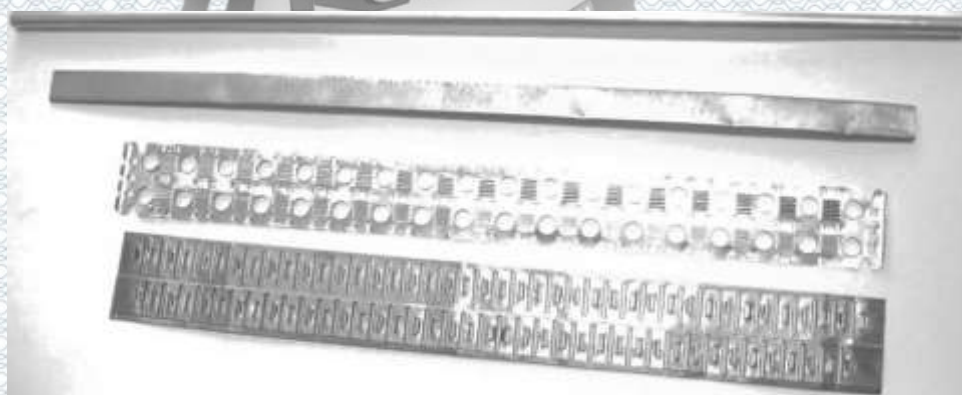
Загальний вигляд оребрюючої пластини і трубки радіаторів
